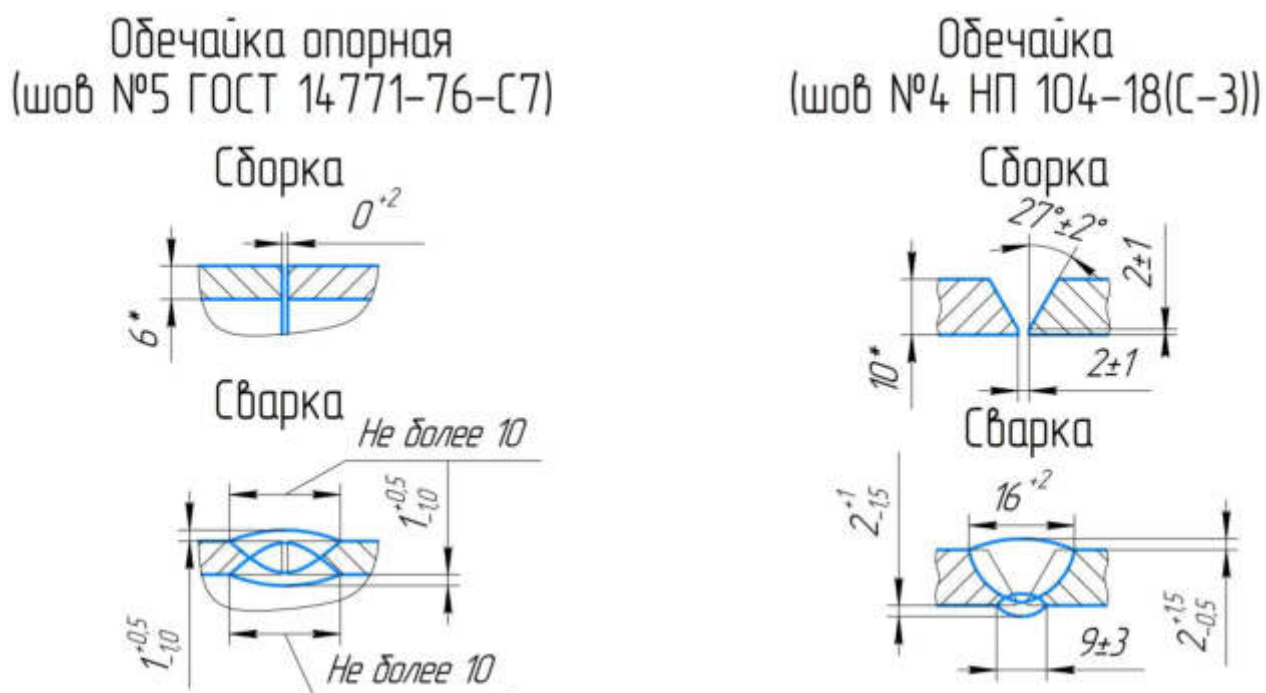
Виды швов при сборке и при сварке обечаек
